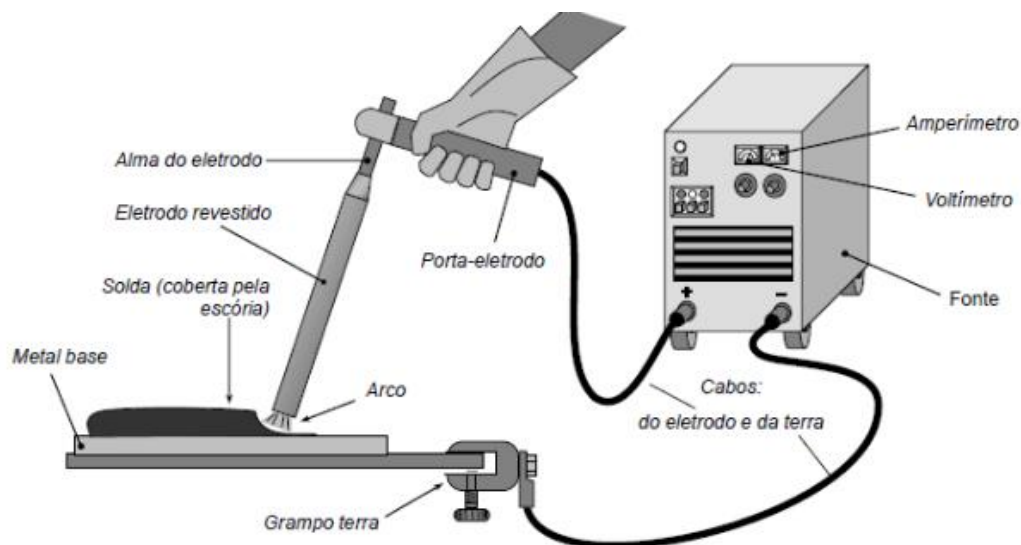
Esquema do processo de soldagem com eletrodo revestido
